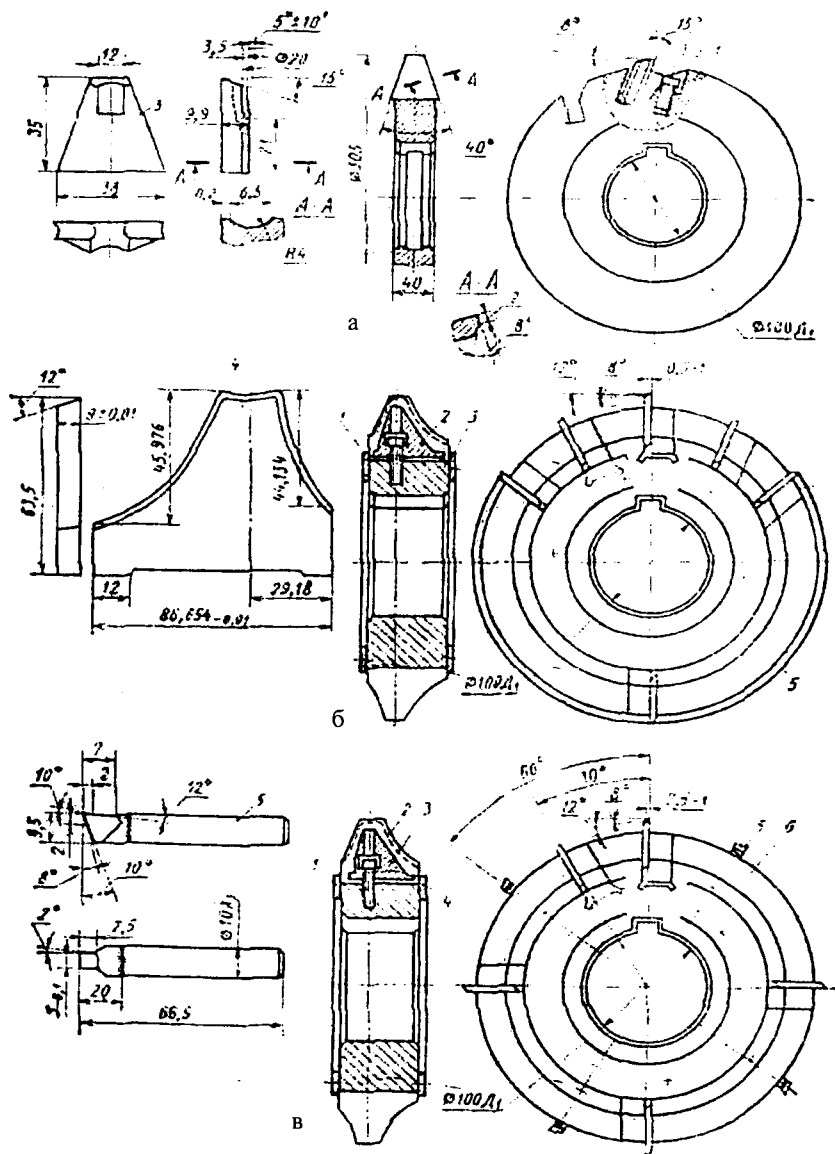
Комплект фрез для обробки профілю ведучого ротора гвинтового компресора на верстаті "Холройд": а – фреза дискова чорнова для попередньої обробки (1 – корпус; 2 – клин; 3 – ніж); б – фреза дискова напівчистова (7, 3 – кільця; 2 – клин; 4 – ніж; 5 – корпус); в – фреза дискова чистова (1, 4 – кільця; 2 – ніж; 3 – клин; 5 – різець; 6 – корпус).
